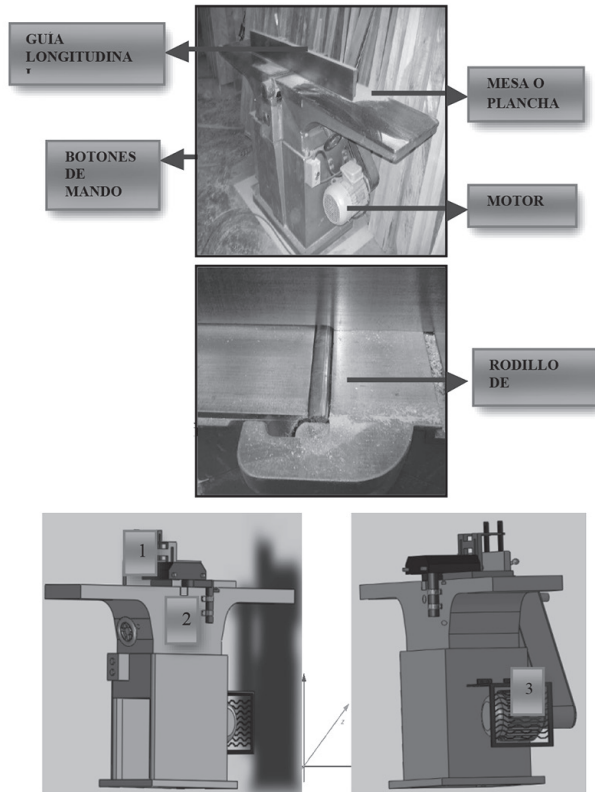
Análisis de Resguardos Máquina Planeadora, Fuente el Autor
